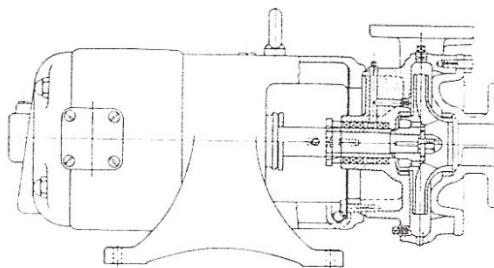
Bomba con acoplamiento compacto (montada en el motor)
